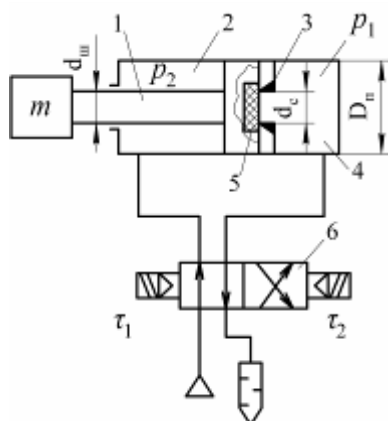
Ударный пневмоцилиндр со встроенным резервуаром (схема № 1)
